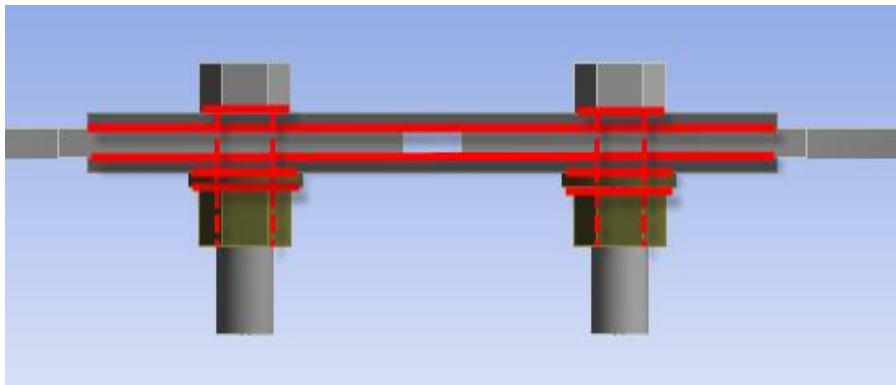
les surfaces des contacts dans l'assemblage boulonnées.
